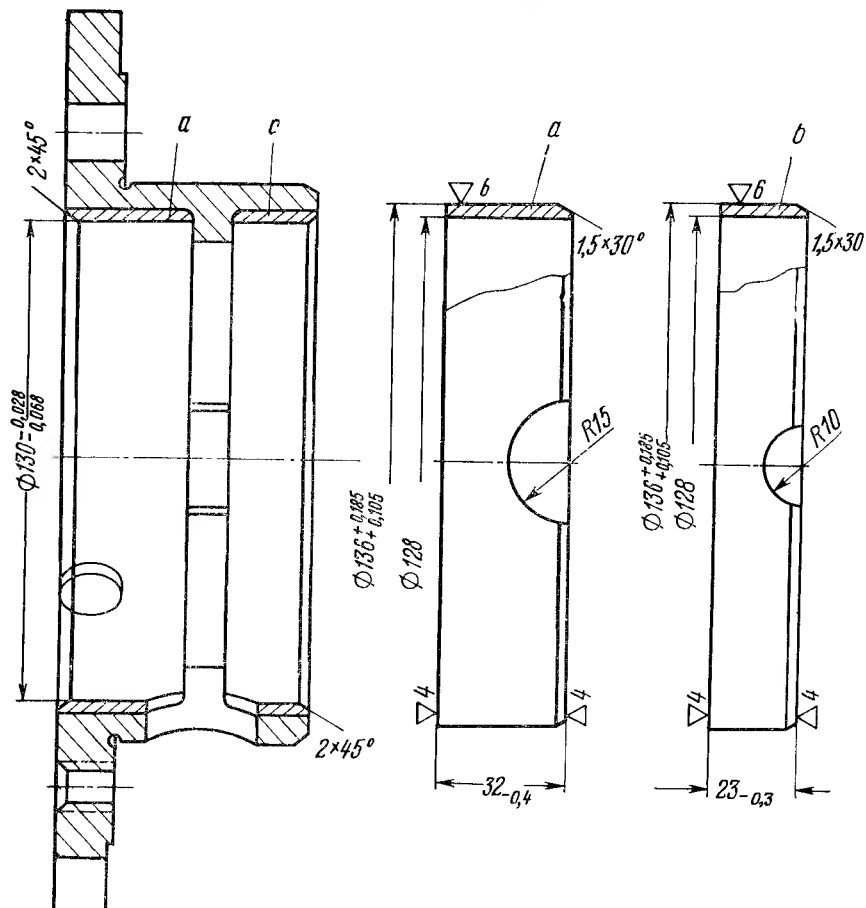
Ремонтные втулки картера подшипников вала ведущей шестерни: а — под наружное кольцо переднего роликового подшипника; б — под наружное кольцо заднего роликового подшипника
